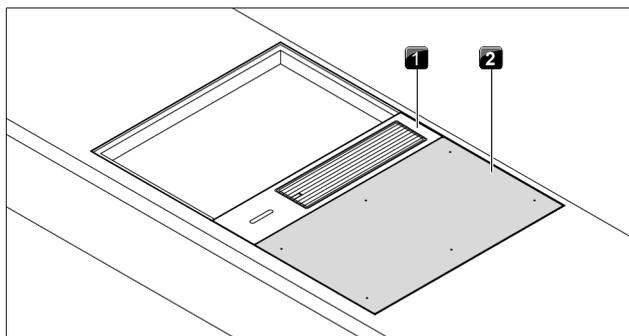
Placa de cocción ajustada junto al extractor de superficie
